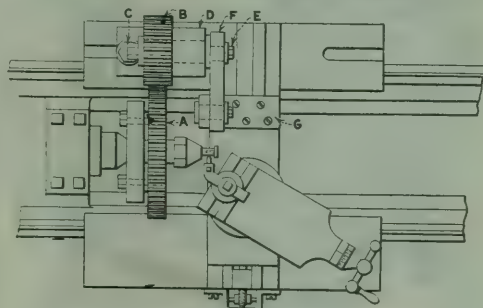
APARATO EMPLEADO PARA TORNEAR PIEZAS OVALADAS
